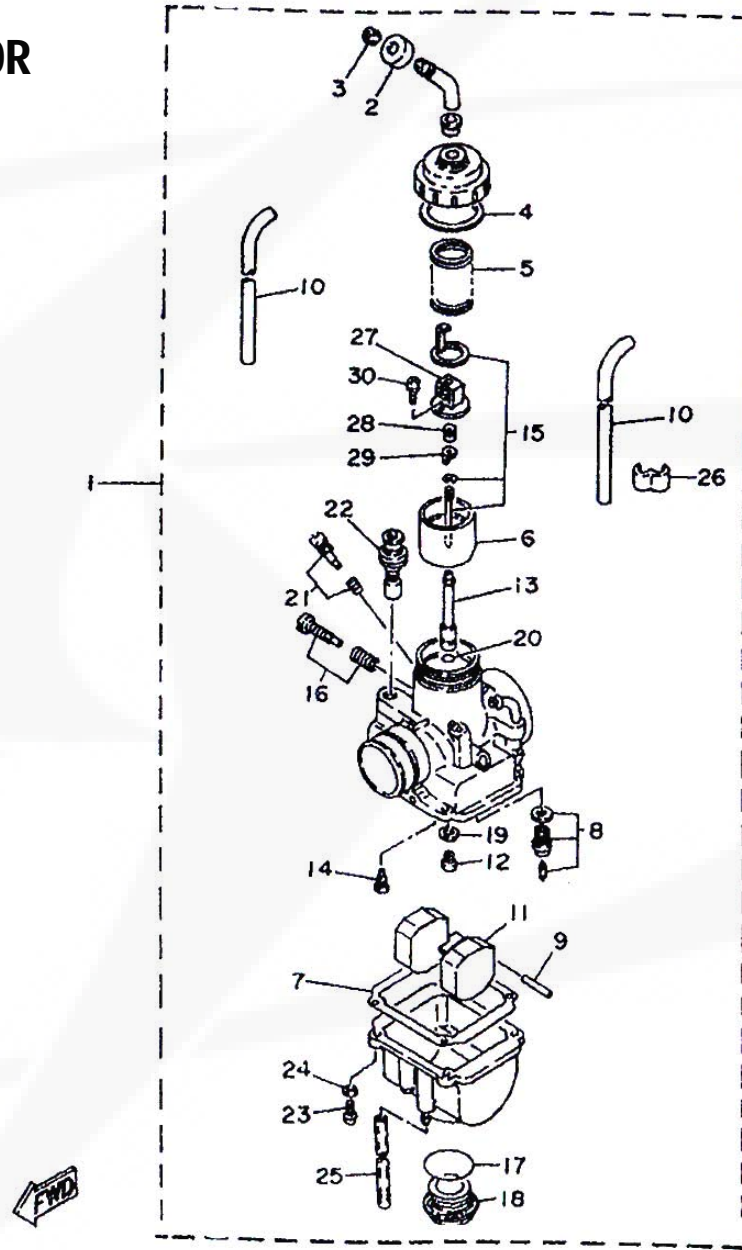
CARBURATEUR / CARBURETTOR / CARBURADOR
